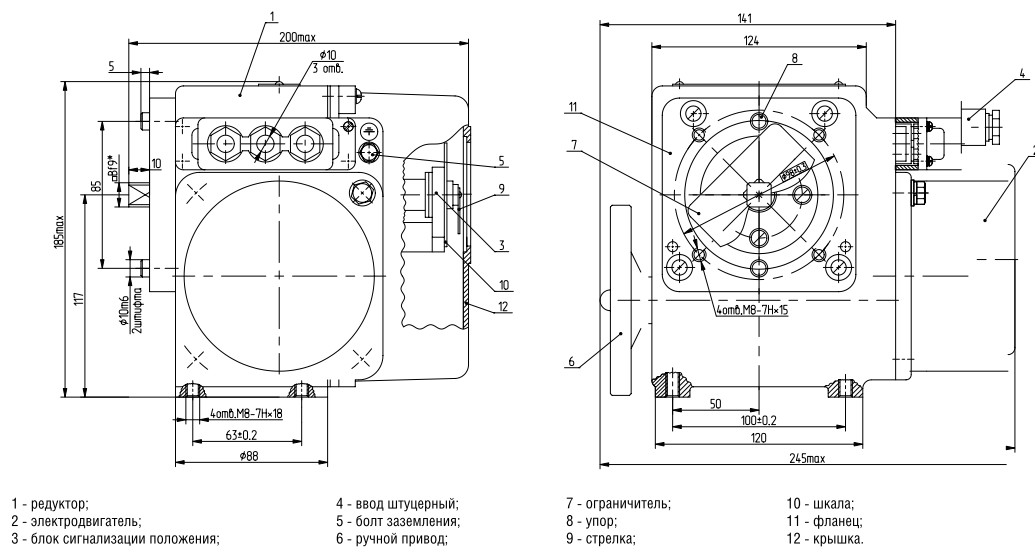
Габаритные и присоединительные размеры М30Ф-40
